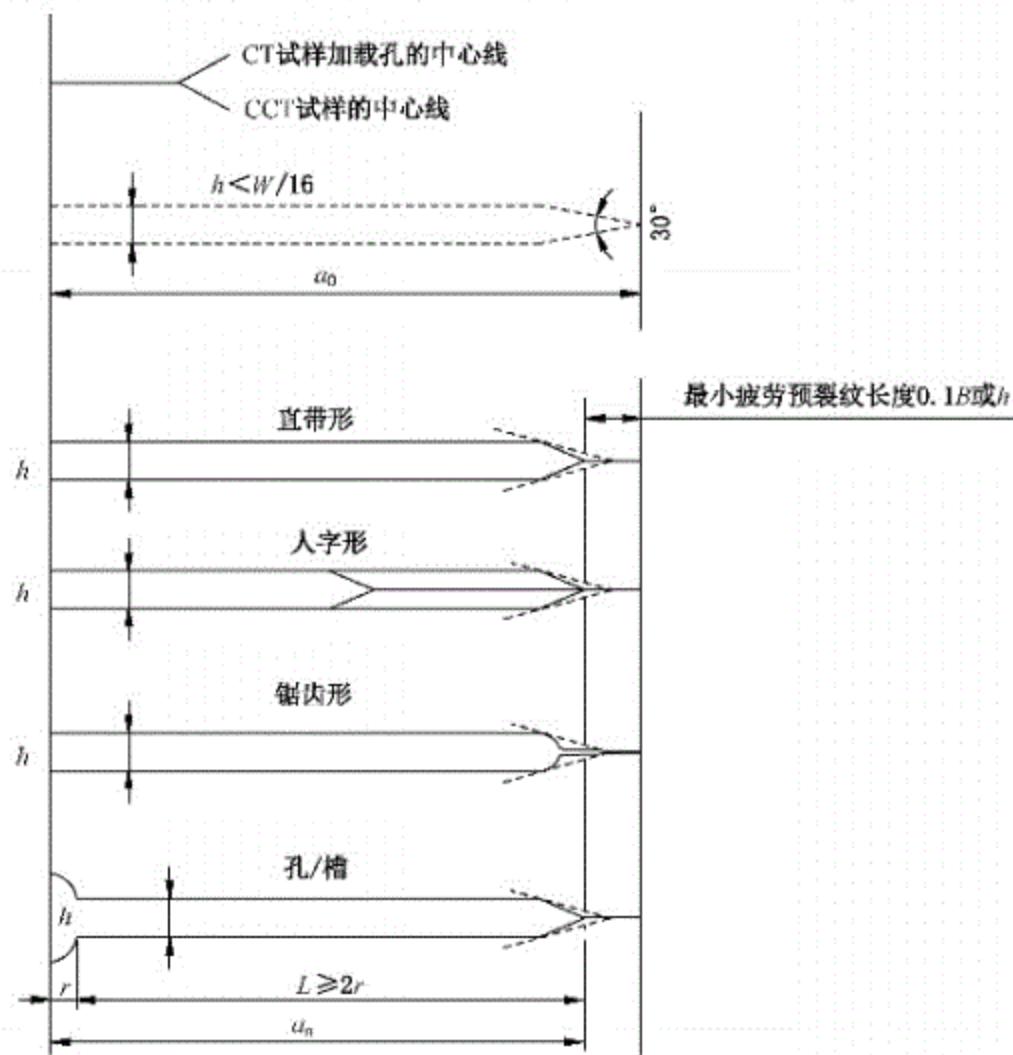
焊接接头疲劳裂纹扩展速率缺口形状和最小预裂纹试样
